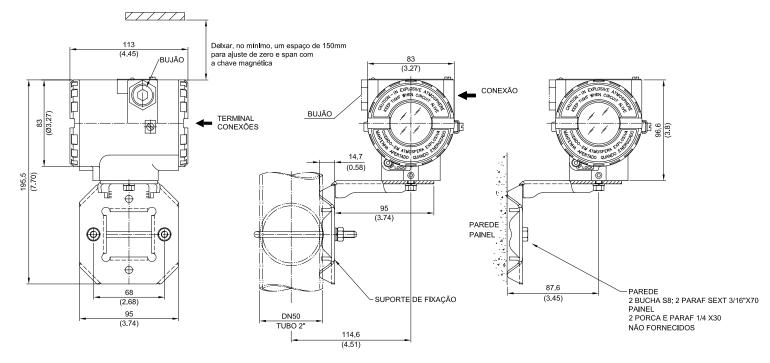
Desenho Dimensional e Posições de Montagem
